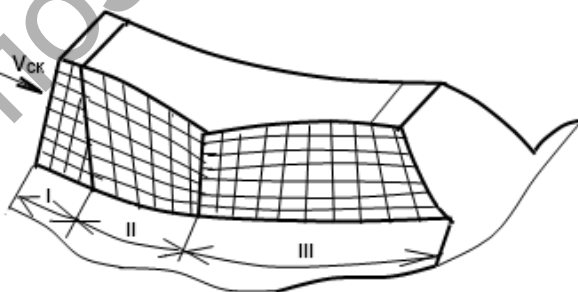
Форма зуба червячного колеса классической глобоидной передачи [37]
